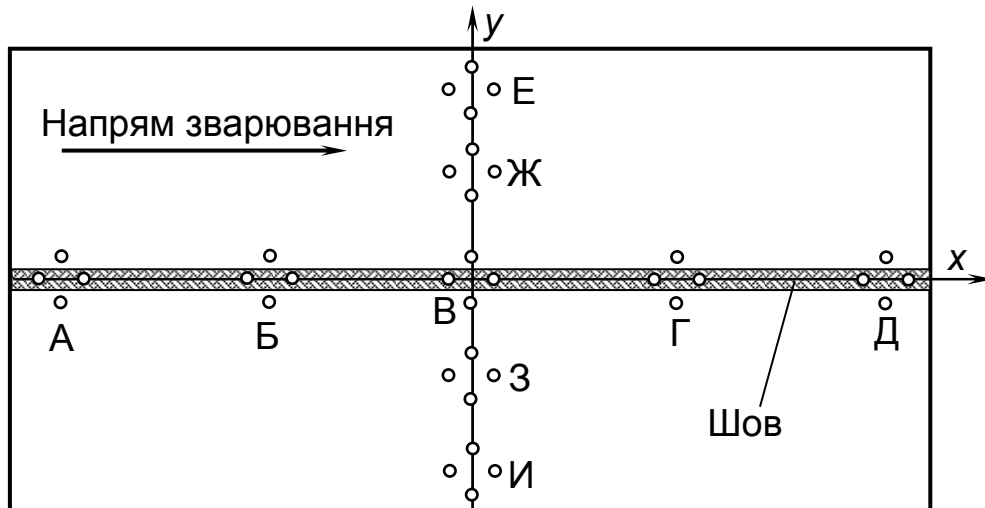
Схема розташування вимірювальних баз і розеток на зварному зразку
